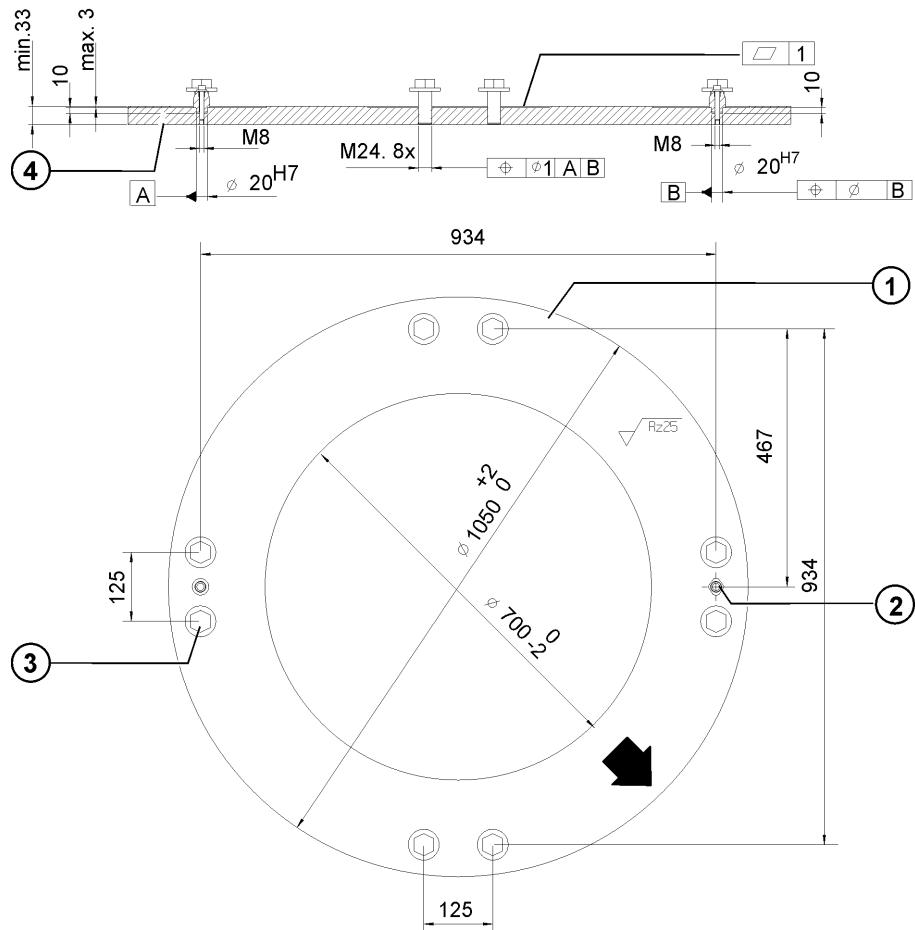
Maschinengestellbefestigung, Maßzeichnung
